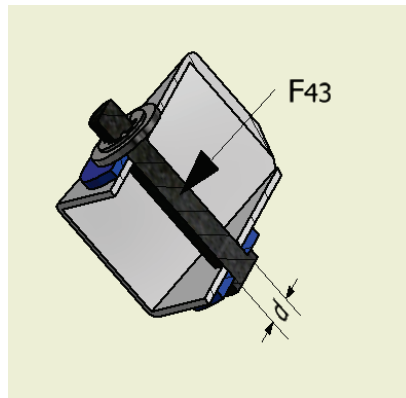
Fuerzas actuantes en pasador entre manivela y soporte espaldar.
